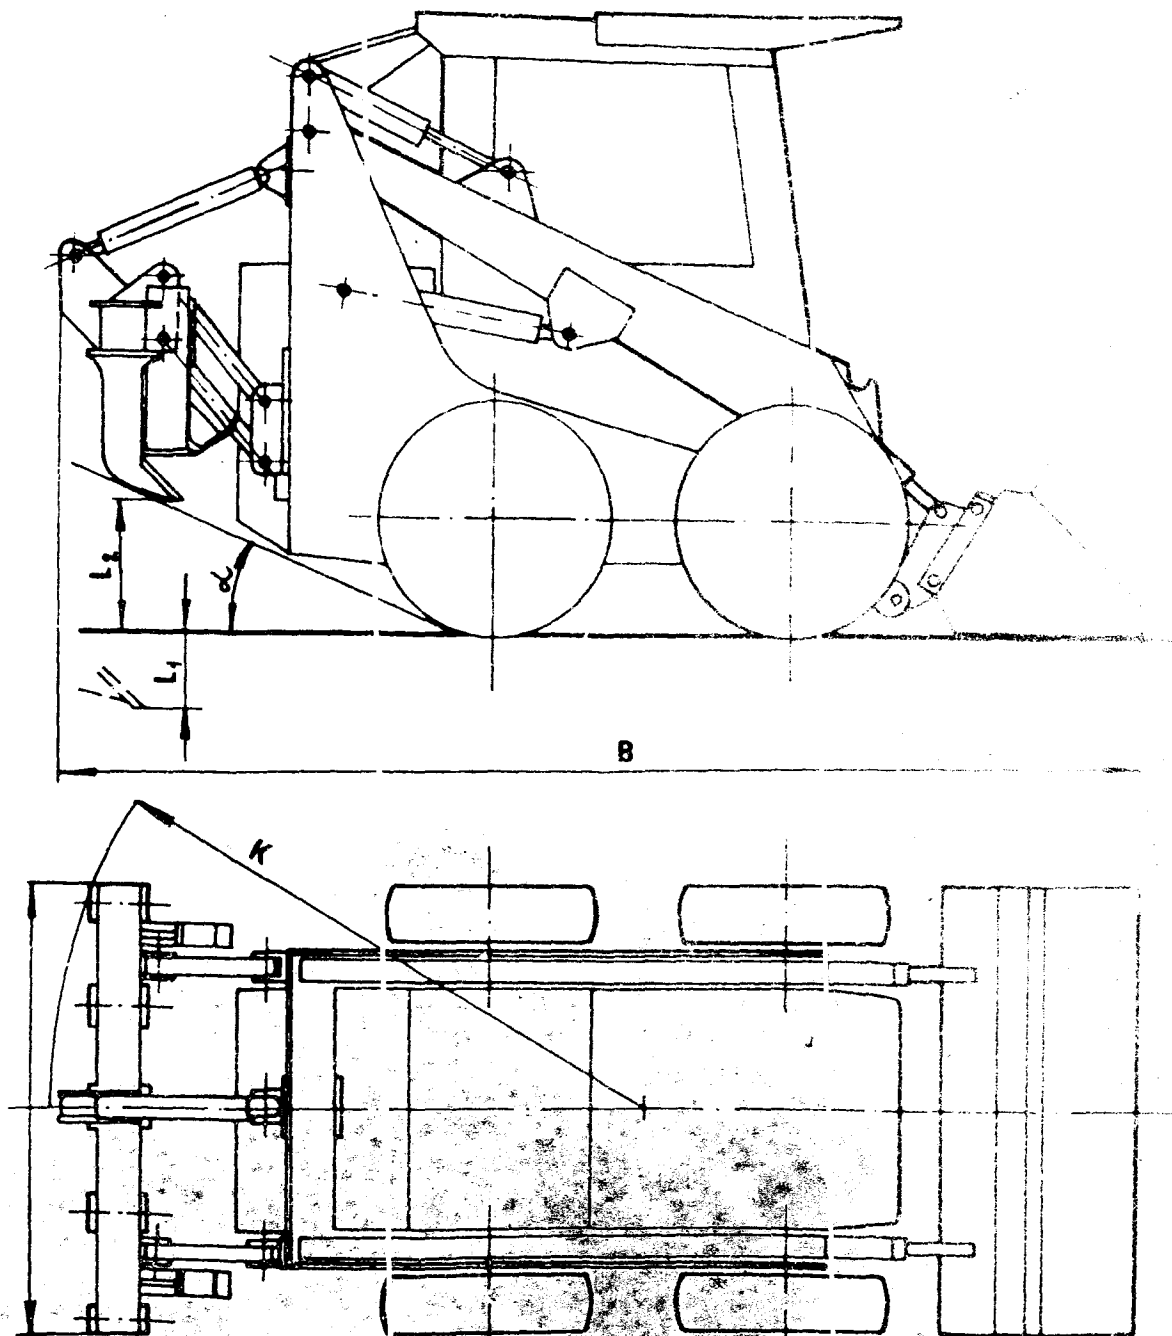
Габаритный эскиз погрузчика с рыхлителем
